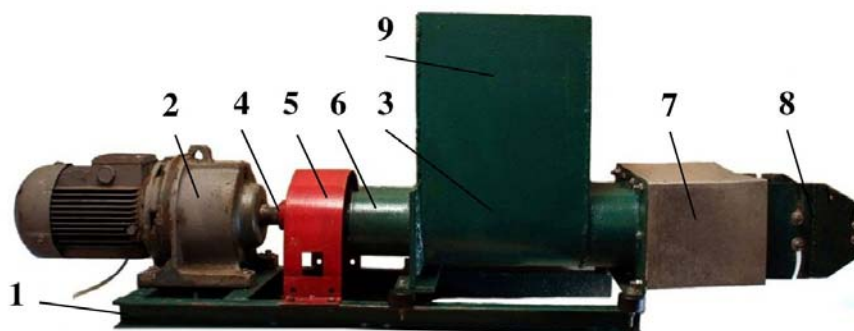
Зовнішній вигляд двогвинтового пресу для зневоднення пивної дробини. 1 - станина; 2 - мотор-редуктор; 3 - корпус пресу; 4 - муфта ланцюгова; 5 - передача зубчата; 6 - рукав підшипниковий; 7 - конфузори; 8 - насадка віджимаюча з регулюючими пластинами; 9 – бункер завантажувальний
